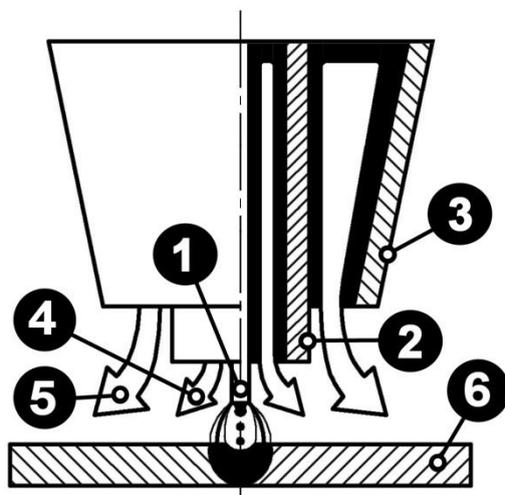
Схема сварки в условиях комбинированной газовой защиты: 1 – электродная проволока; 2 – центральный газовый канал; 3 – кольцевой газовый канал; 4 – внутренний поток газа; 5 – кольцевой (защитный) поток газа; 6 – свариваемое изделие
